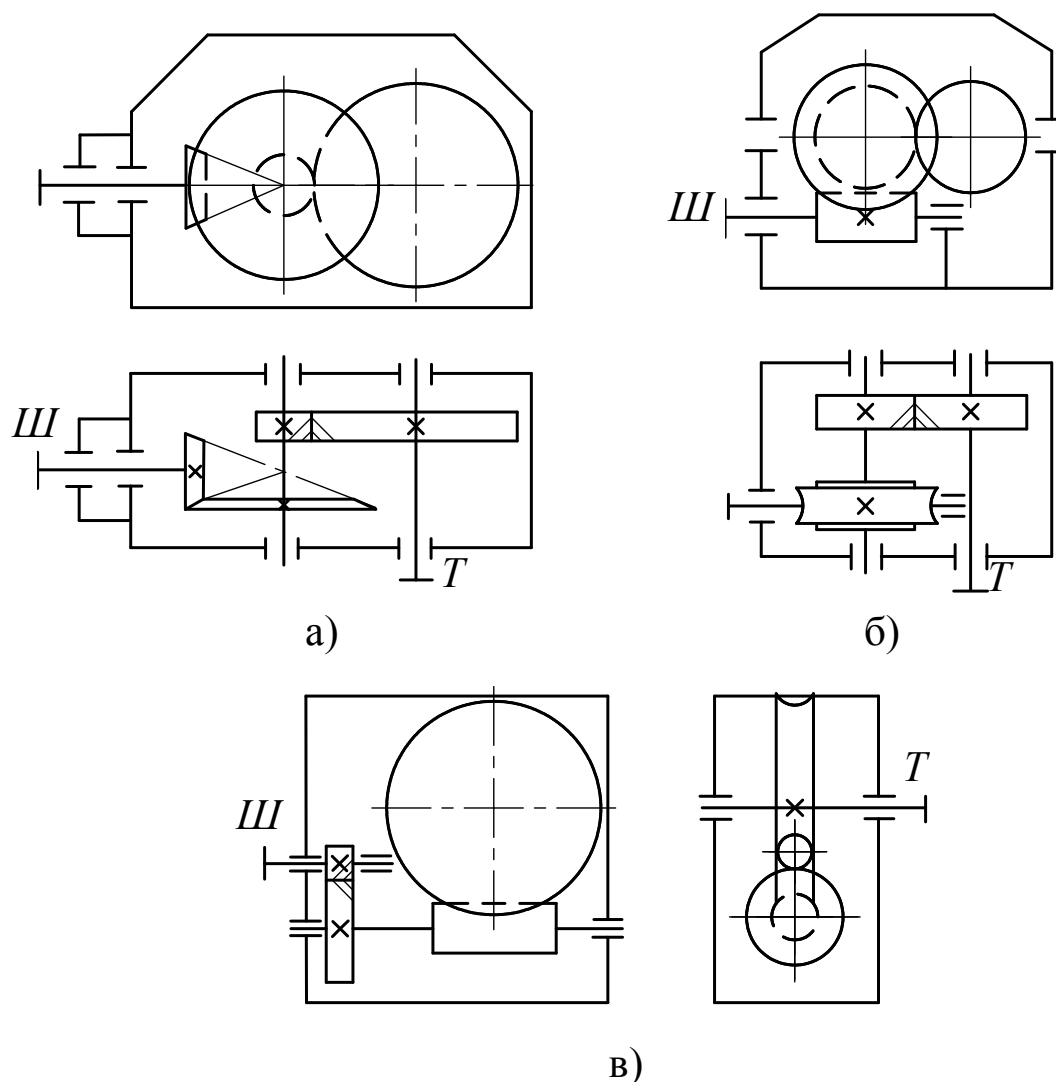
Кинематические схемы двухступенчатых редукторов различных типов: а) коническо-цилиндрический редуктор; б) червячно-цилиндрический редуктор; в) цилиндрическо-червячный редуктор, (Ш - быстроходный вал, Т - тихоходный вал)
